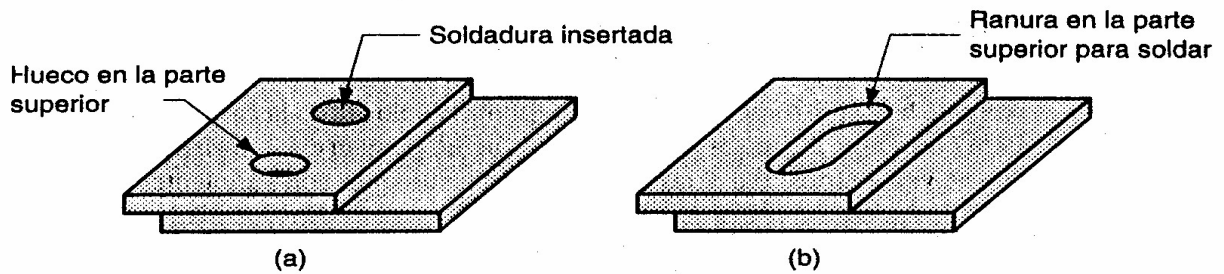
(a) Soldadura con inserto y (b) soldadura en ranura.
